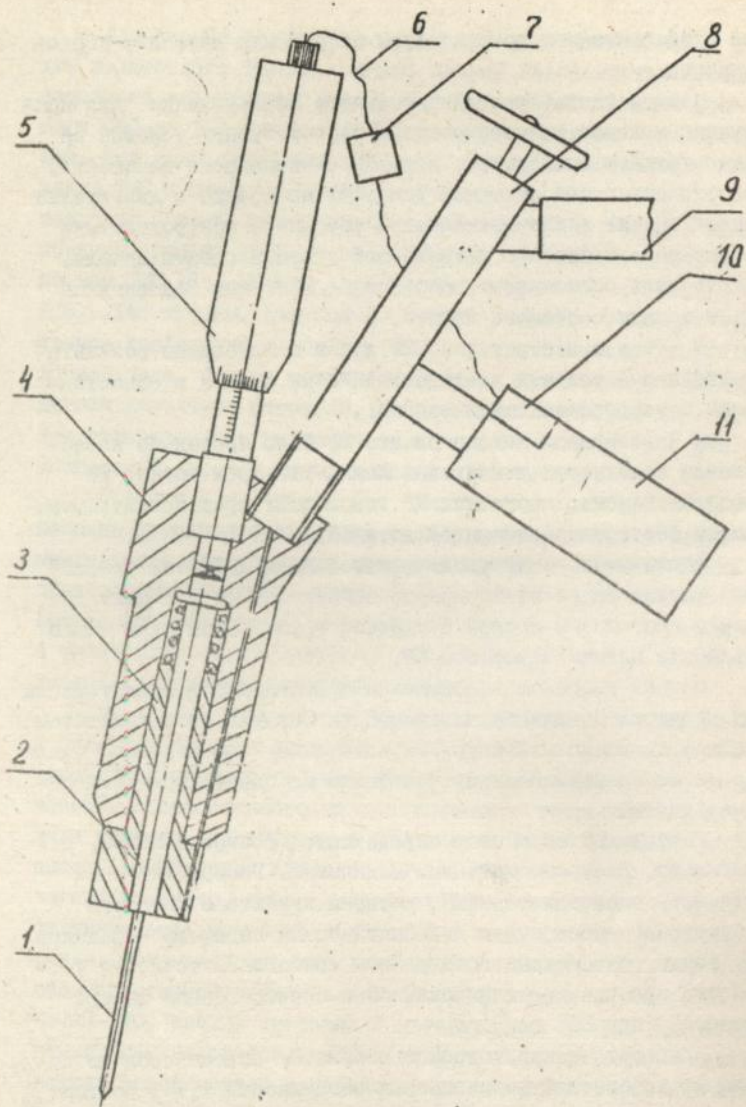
Схема устройства: I-щуп; 2-плунжер; 3-гильза плунжера; 4-корпус форсунки; 5-микрометрический винт; 6-проводник; 7-элемент питания; 8-кран воздушный; 9-шланг отводной; 10-светодиод; 11-манометр
